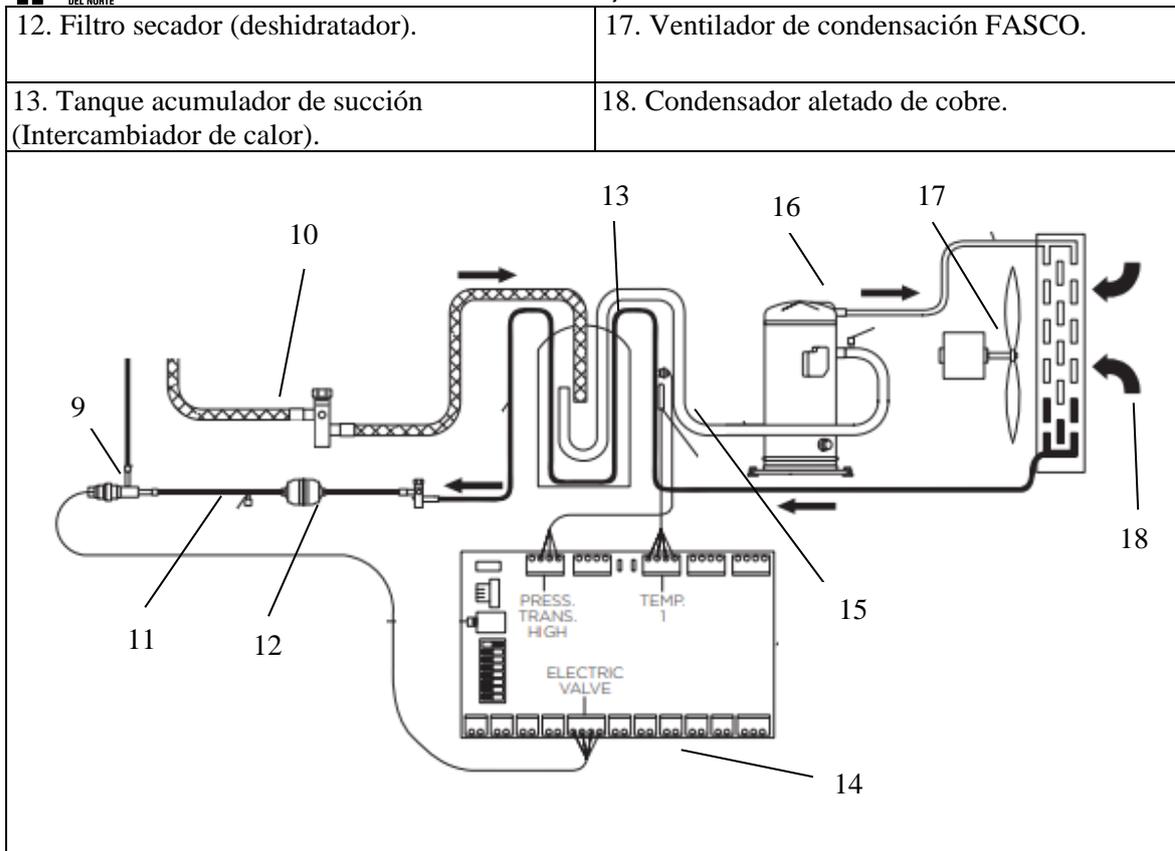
Despiece de partes generales de tanque de enfriamiento 1000 galones.
